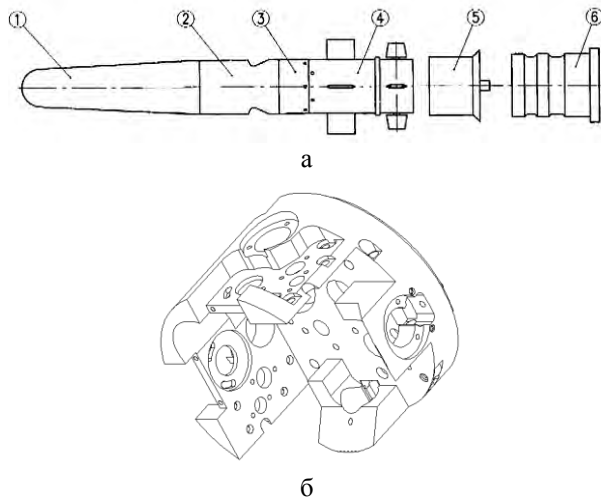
Керована ракета: а – схема; 1, 2 – головна й середня частини; 3, 4 – блоки корпусу; 5, 6 – блоки хвостової частини, б – корпусна деталь, що одержують механічною обробкою різанням
